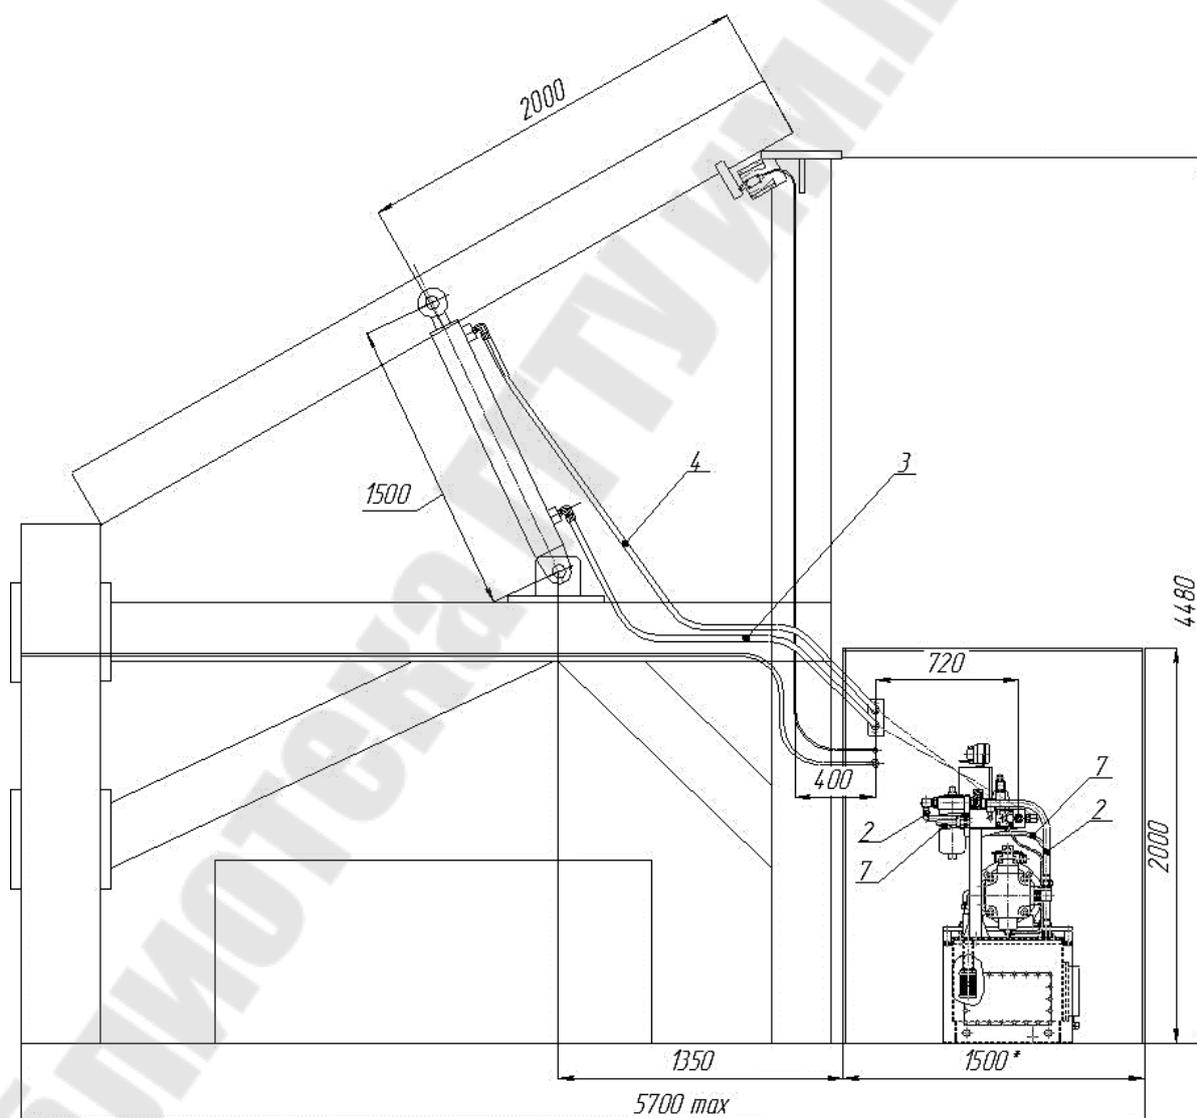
Монтажная схема трубопроводов на линии переработки шлака (вид сбоку)
